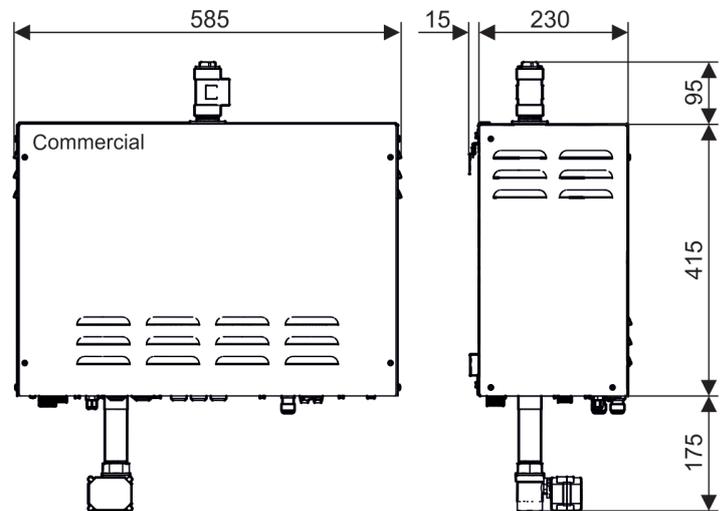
Dampferzeuger Typ Tylö Steam Commercial, Maßangaben in Millimetern
